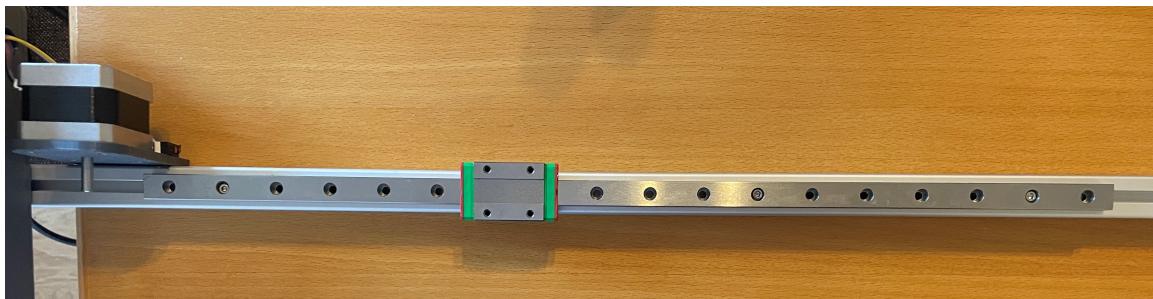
Neunter Schritt: Montage der Linearführung
